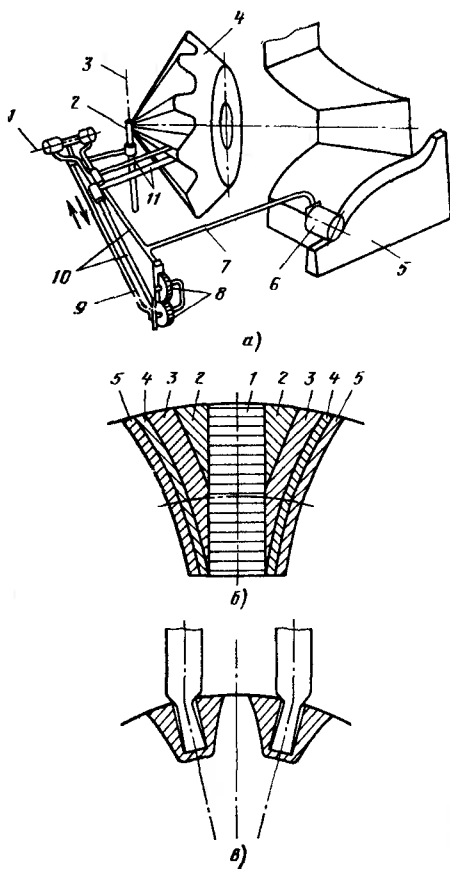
Нарезание конических зубчатых колес по шаблону
